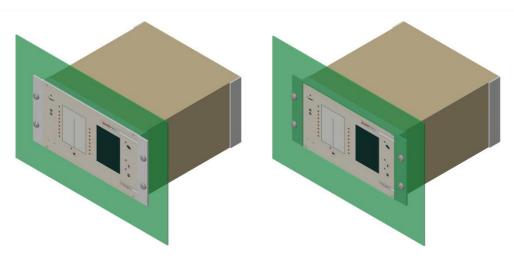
D pour le montage en rack d'un appareil 9" 1/2 (42TE) (a - par l'avant ; b - par l'arrière)
